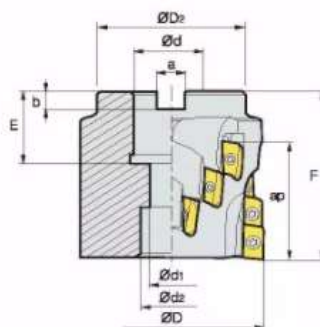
Чертеж и таблица размеров торцевой фрезы
